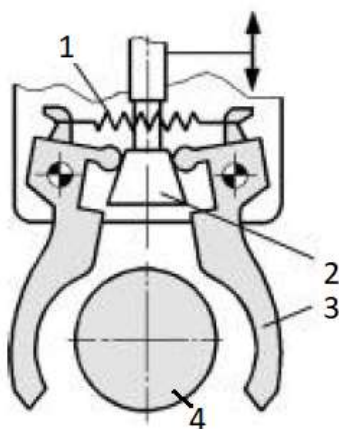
Schéma efektoru s pneumatickým pohonem a ozubeným převodem [20]
